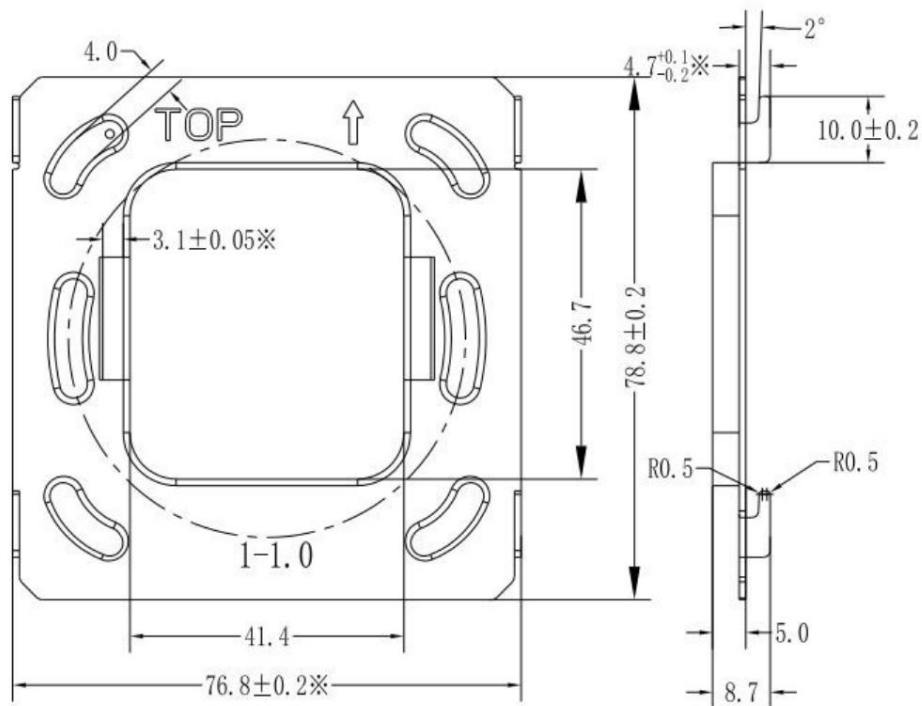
Dimensão da placa de metal de CHTF-4.0/15.3.2x
